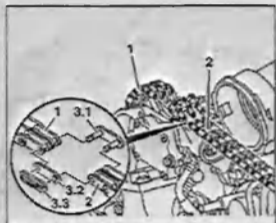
Присоедините новую цепь 2 к старой 1 с помощью звена 3.1 и промежуточной пластины 3.2 и наружной пластины 3.3.
